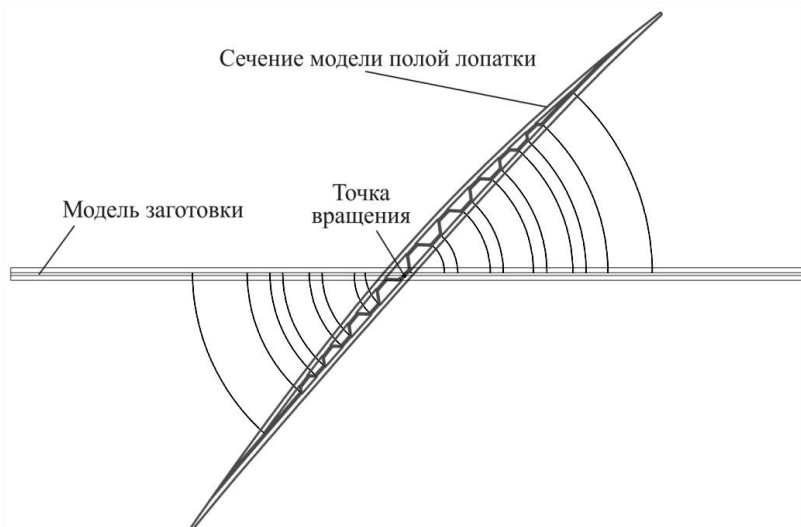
Схема для определения расположения зон сварки нижнего и среднего листа заготовки полый лопатки вентилятора
